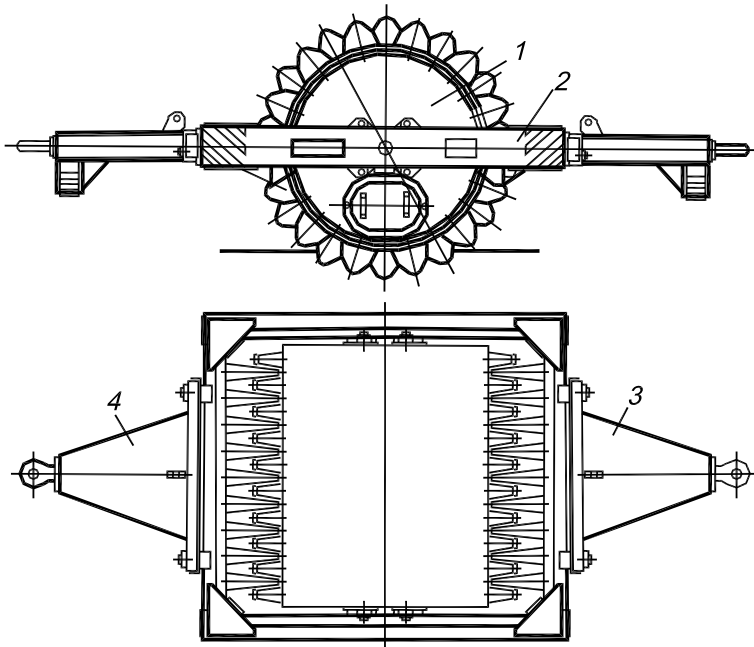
Общий вид прицепного катка ДУ-26А
